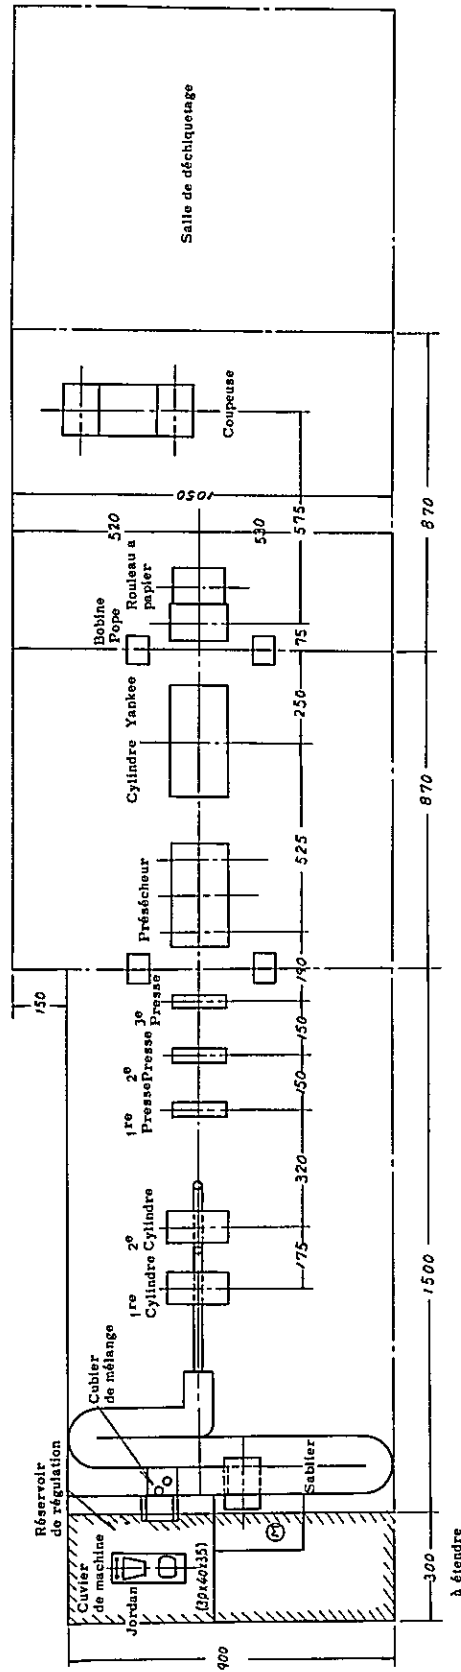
Procédé de Remontage de la Machine à Papier à la P.C. d'Ain-El-Hadjar
